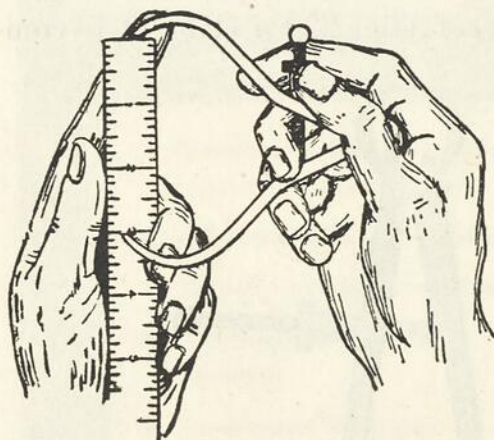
Réglage d'un compas à ressort extérieur (South Bend Lathe Works)
